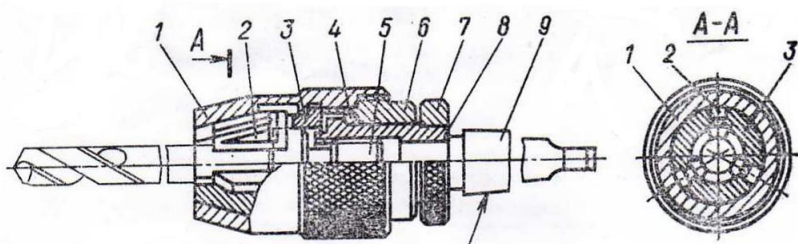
Сверлильный трехкулачковый бесключевой патрон
